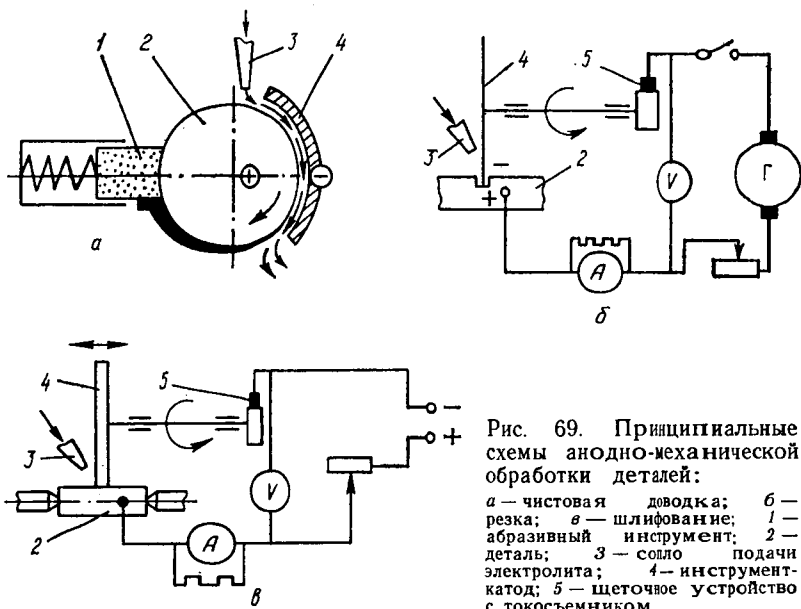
Принципиальные схемы анодно-механической обработки деталей:
